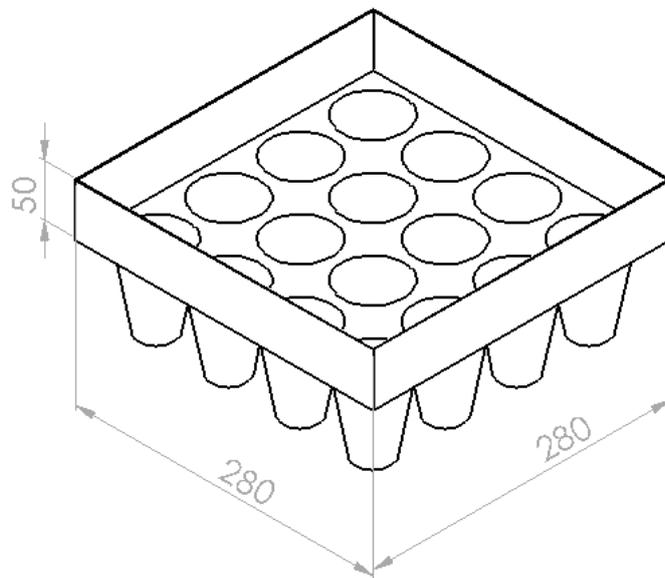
Dimensiones de molde (Jaba) en milímetros
